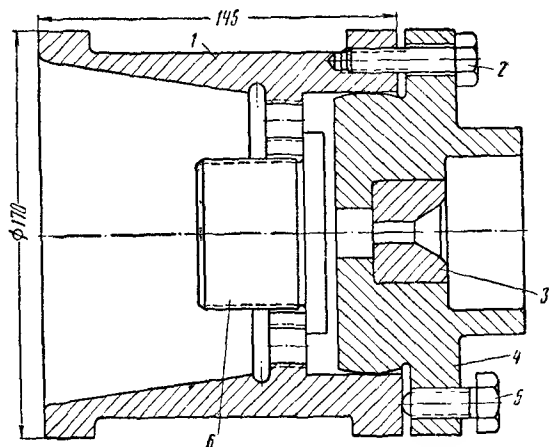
Приспособление для чистовой токарной обработки коллектора электровозного двигателя:
